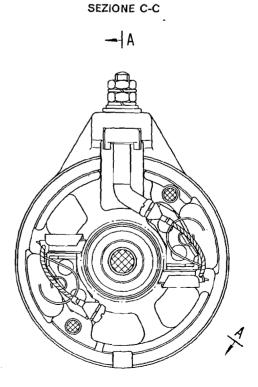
Sezione trasversale e vista del supporto lato collettore.
